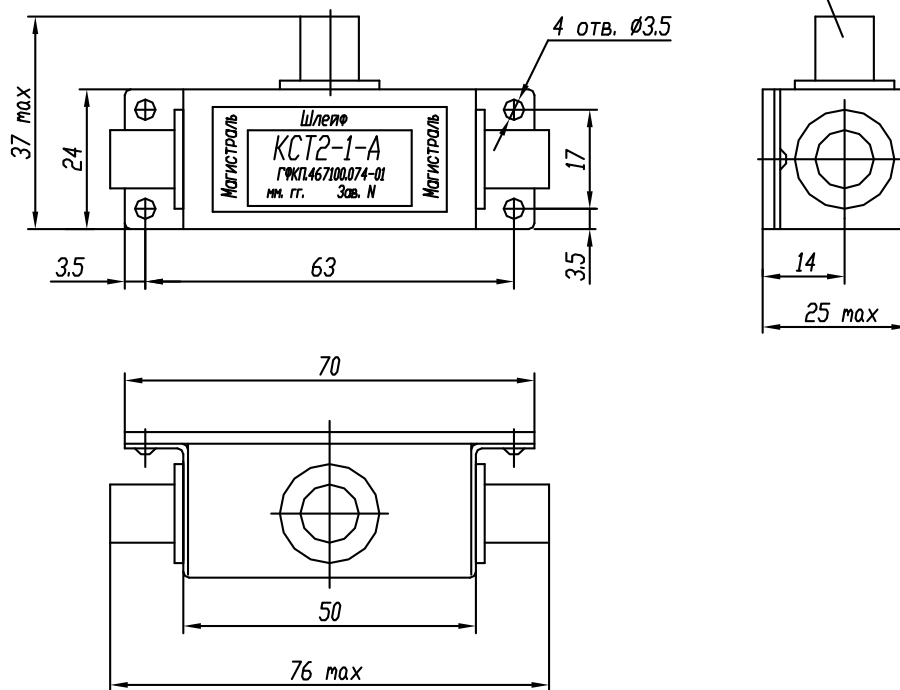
Габаритный чертеж коробки соединительной КСТ2-1
